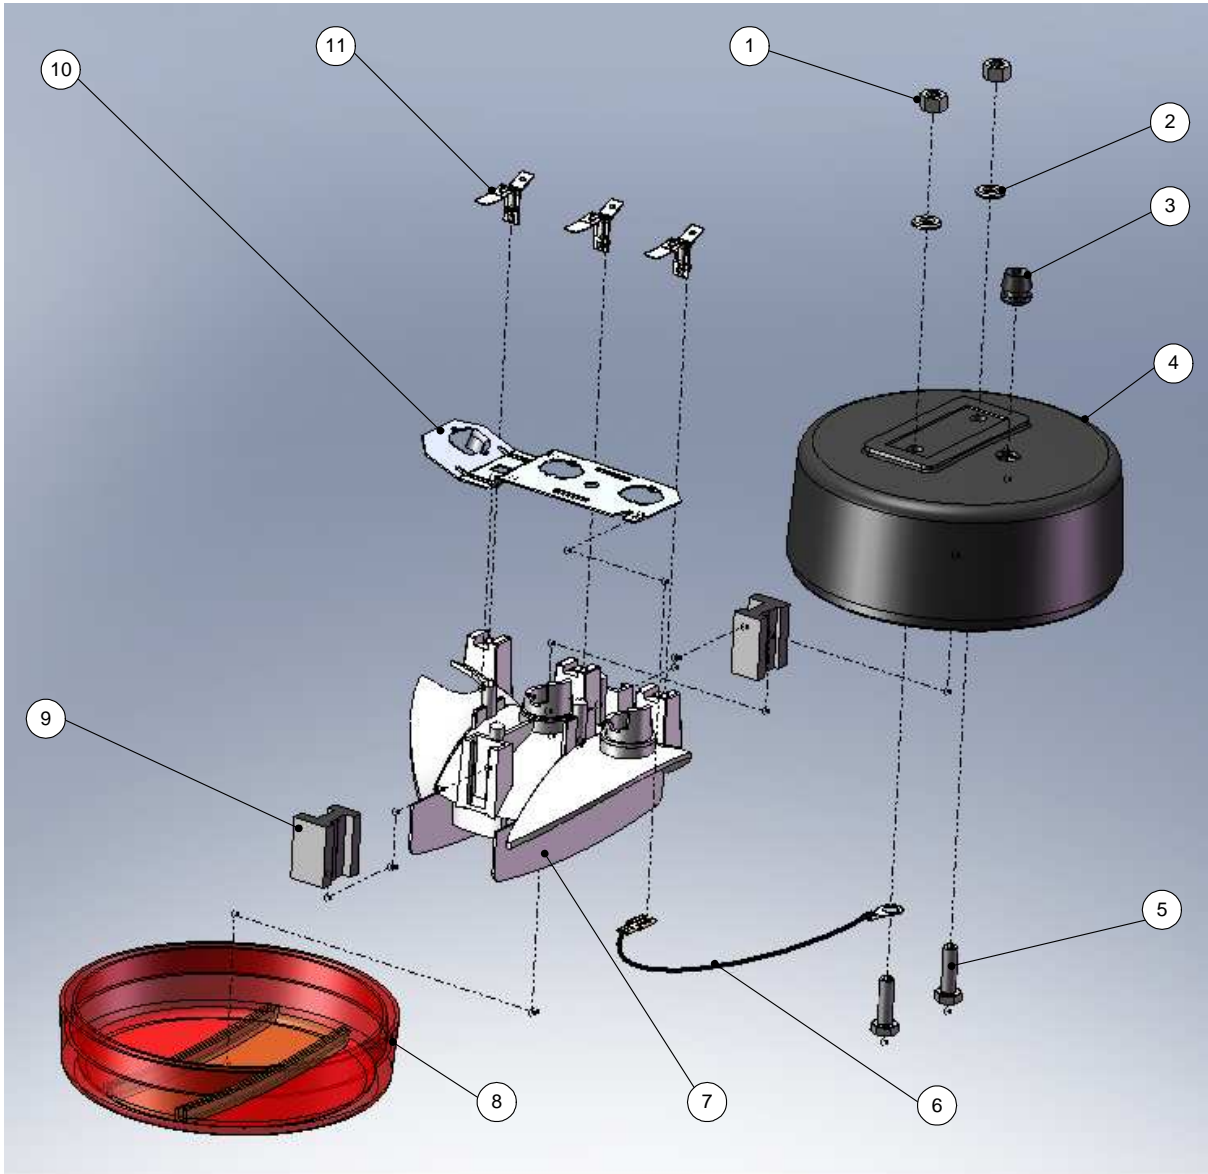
Vista explodida do farolim "Olho de Boi" remodelado
